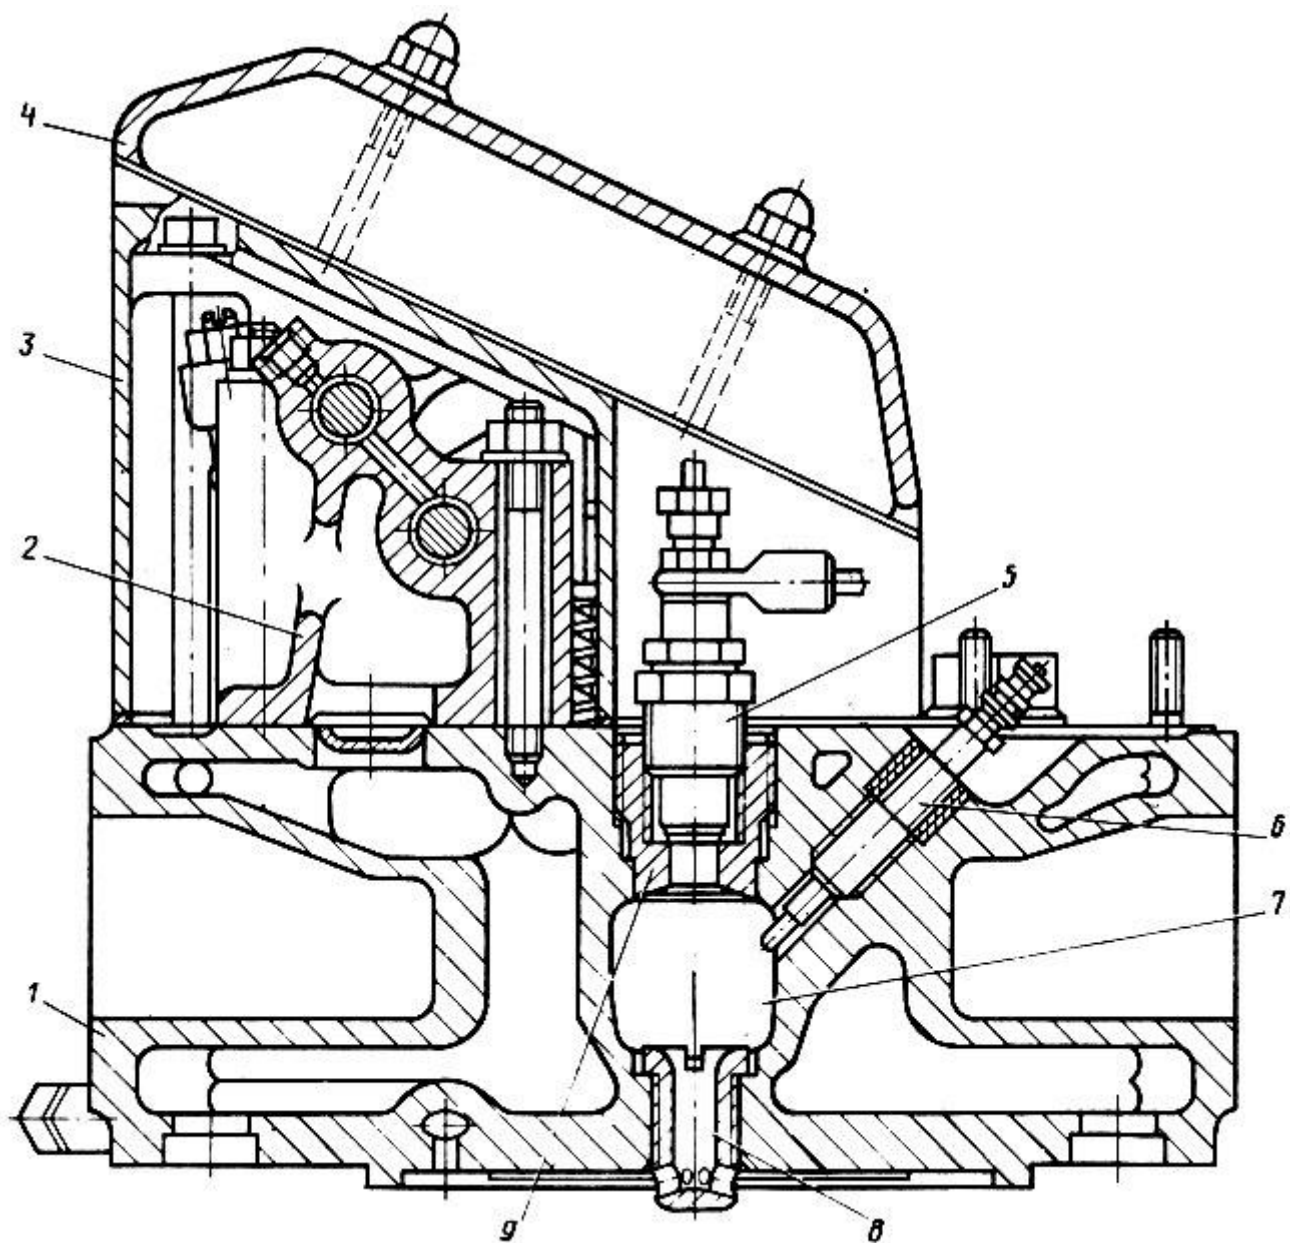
Головка цилиндра: 1 - головка блока; 2 - стойка коромысел; 3 - клапанная коробка; 4 - крышка клапанной коробки; 5 - форсунка; 6 - свеча накаливания; 7 - предкамера; 8 - сопло; 9 - втулка форсунки
